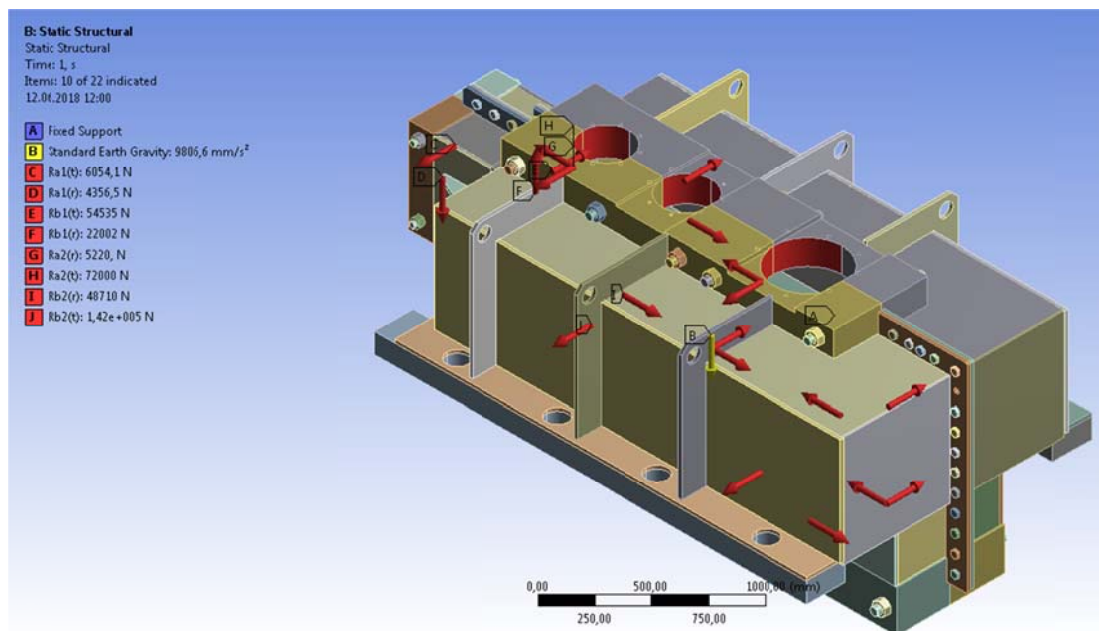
3D-модель сборки сварного корпуса универсального редуктора вертикальной прокатной клетки
